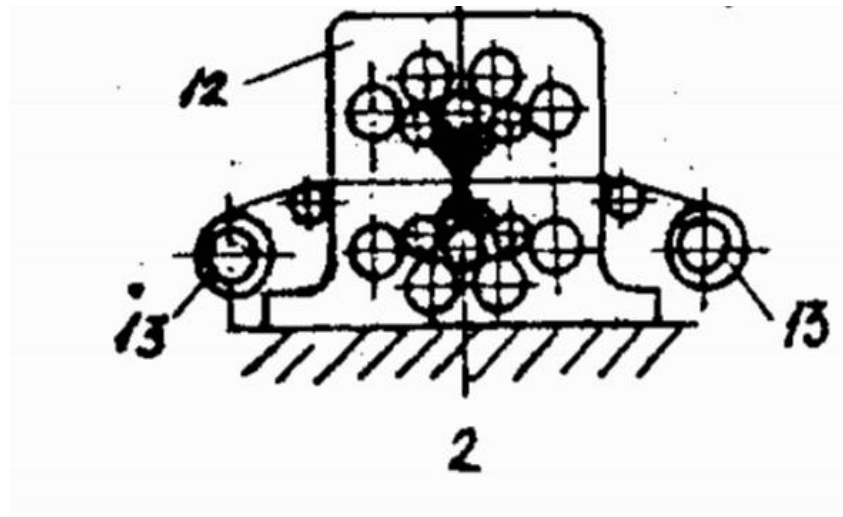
Схема багатоклітьового реверсивного стану: 2 – стикозварювальна машина; 12 – двадцятивалкова реверсивна кліть; 13 – моталка
